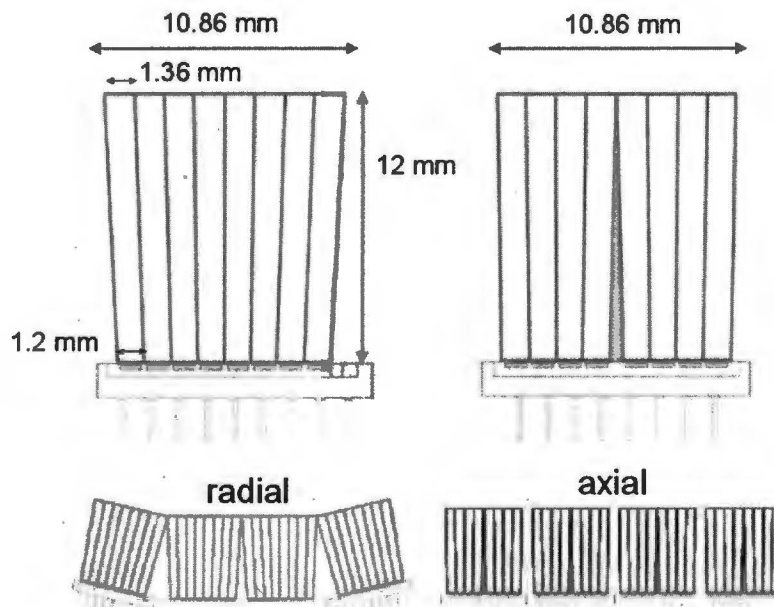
Dessin technique du bloc de scintillateur fabriqué par Proteus inc. ainsi que la disposition envisagée de ces modules dans un anneau complet de détecteurs.
